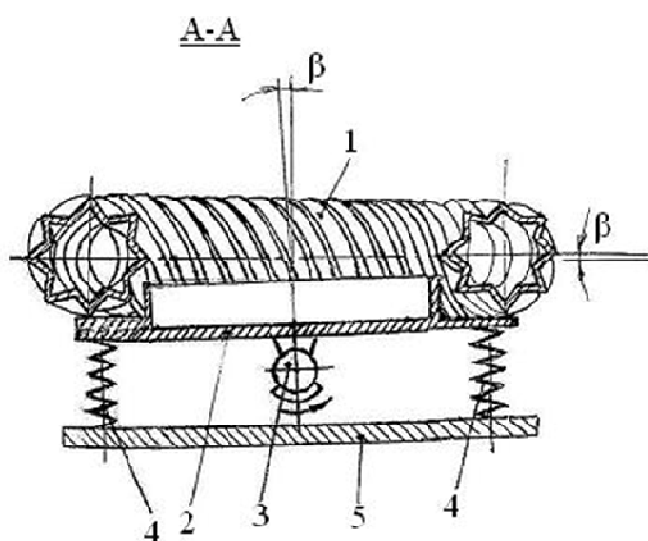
Вибрационная установка для приготовления кормов
